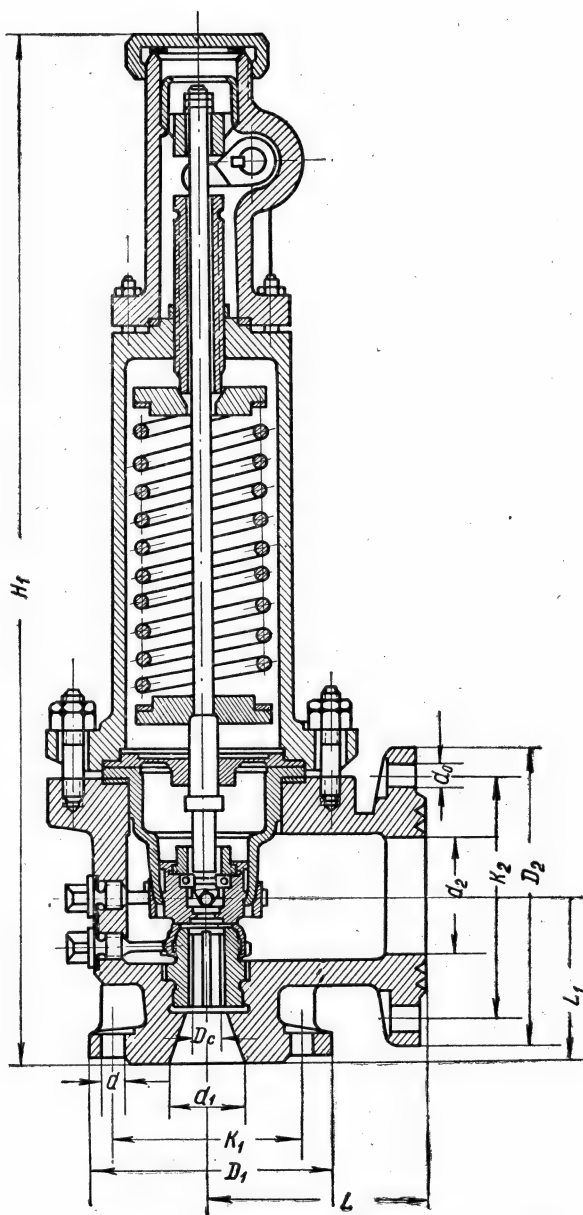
Клапан предохранительный пружинный полноподъемный фланцевый ППК2.
